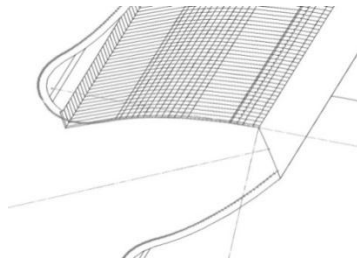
Схема формообразования сетки на обрабатываемой поверхности зубчатого колеса
